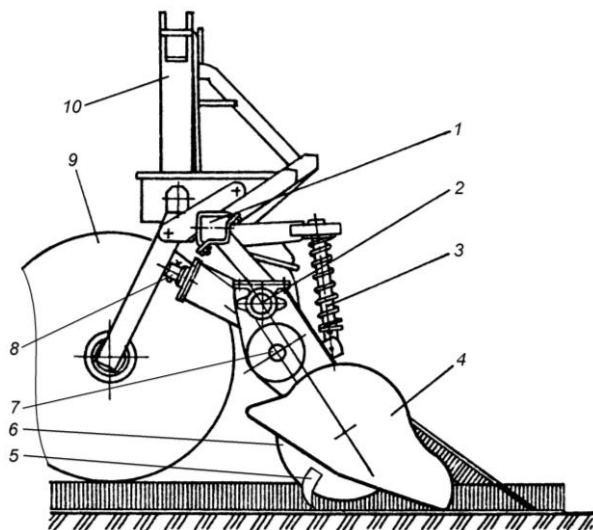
Схема фрезерного культиватора КФ-5,4: 1 – рама; 2 – редуктор; 3 – нажимная штанга; 4 – фрезерная секция; 5 – нож; 6 – диск; 7 – трансмиссионный вал; 8 – механизм привода; 9 – колесо; 10 – замок автосцепки
